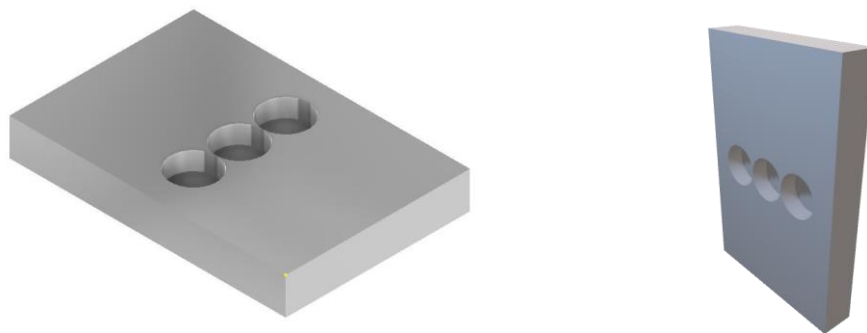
Τρισδιάστατη απεικόνιση αποστολής 28
